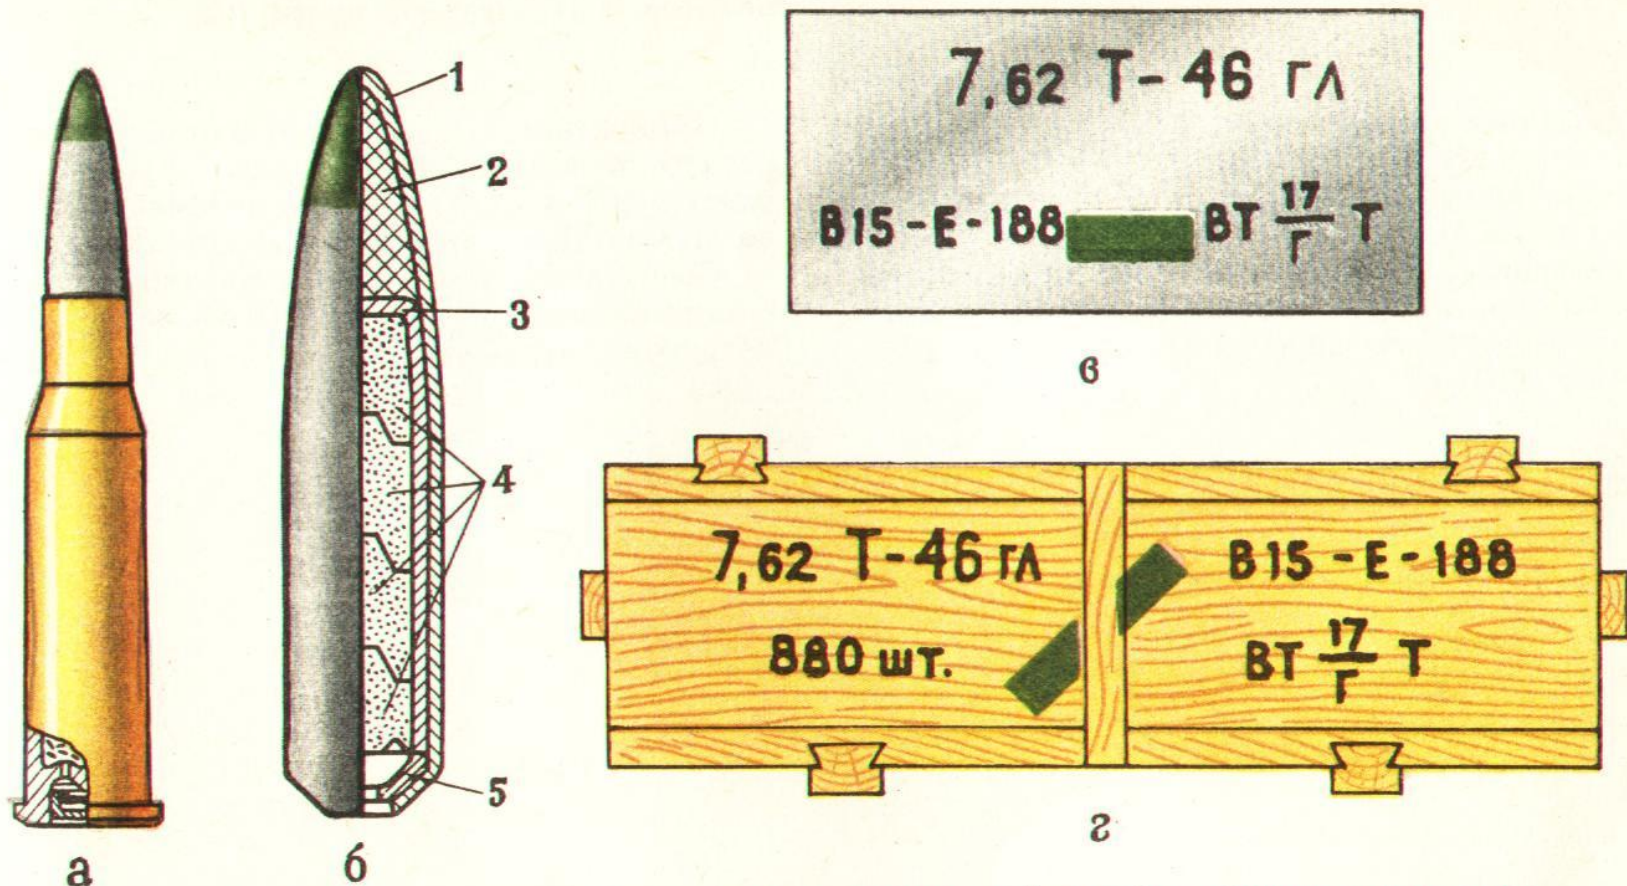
7,62-мм винтовочный патрон с трассирующей пулей и образец маркировки на укупорке:
